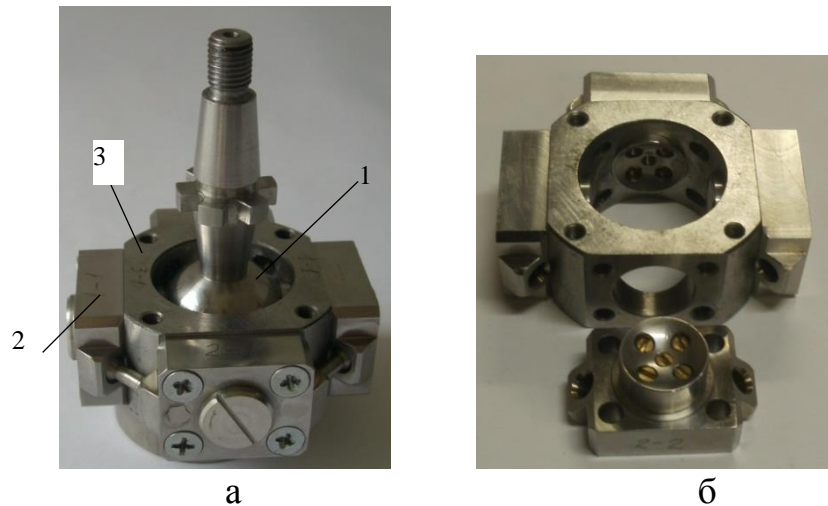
Дослідний зразок гідростатичного шарніра: а – загальний вигляд шарніра; б – фото деталей
